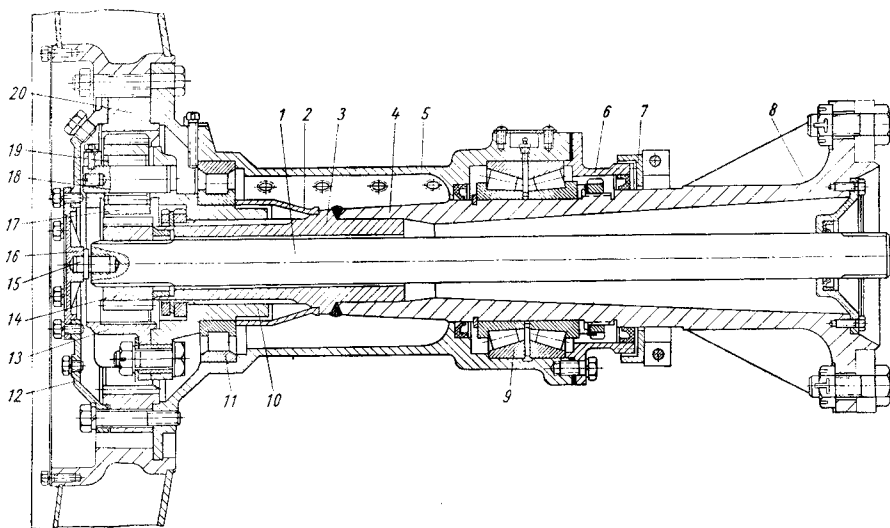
Планетарный редуктор каналокопателя КФН-1200:
